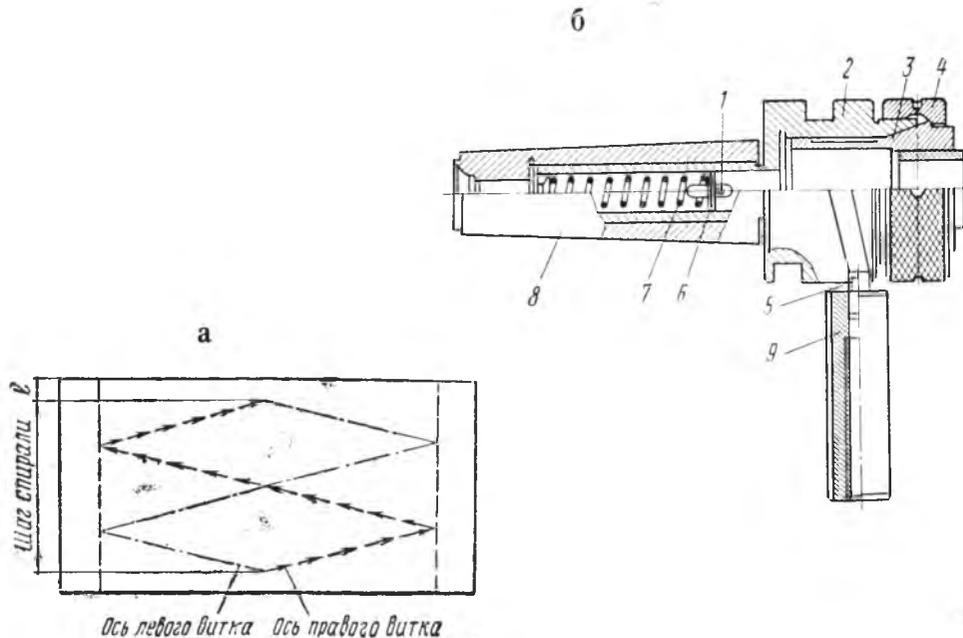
Приспособление для нарезания спиральных смазочных канавок в бронзовых неразъемных подшипниках:
